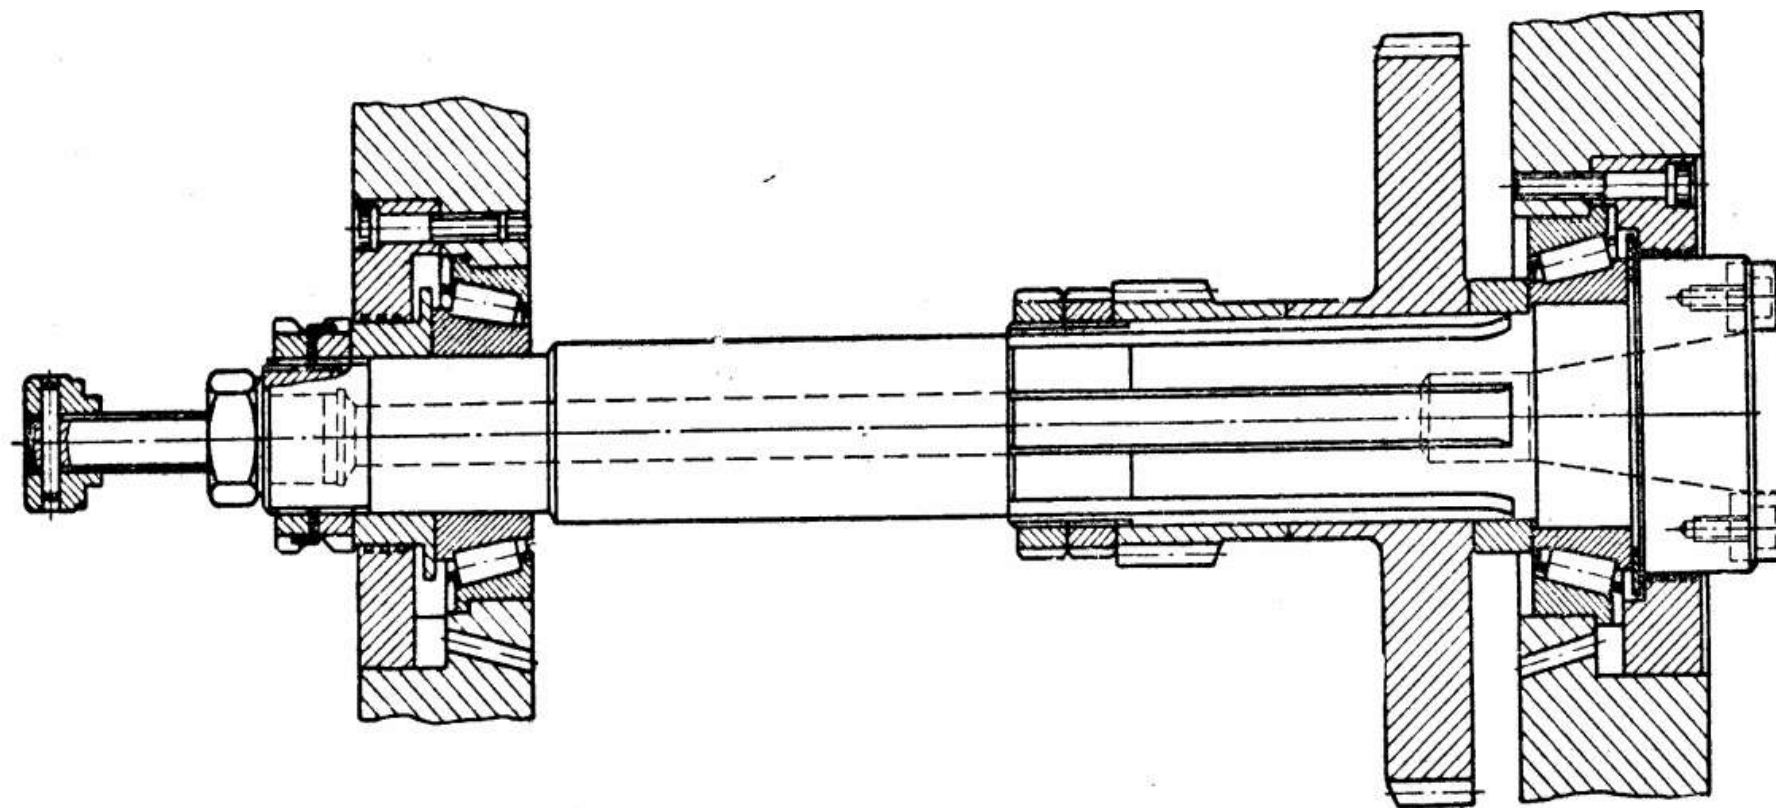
Пример конструкции шпиндельного узла горизонтально-фрезерного станка
